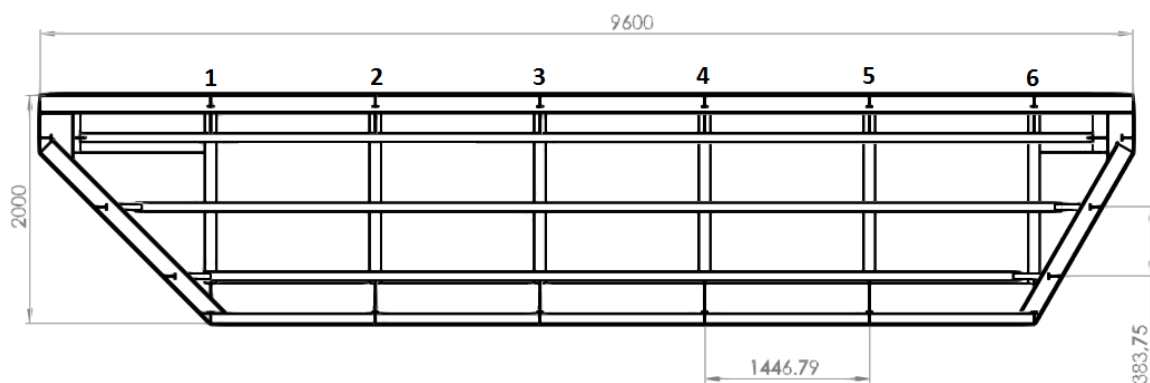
Disposição lateral dos elementos estruturais do módulo central
